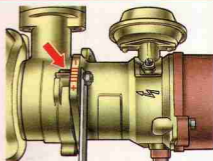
Установка датчика-распределителя зажигания. Стрелкой показан установочный выступ на корпусе вспомогательных агрегатов
